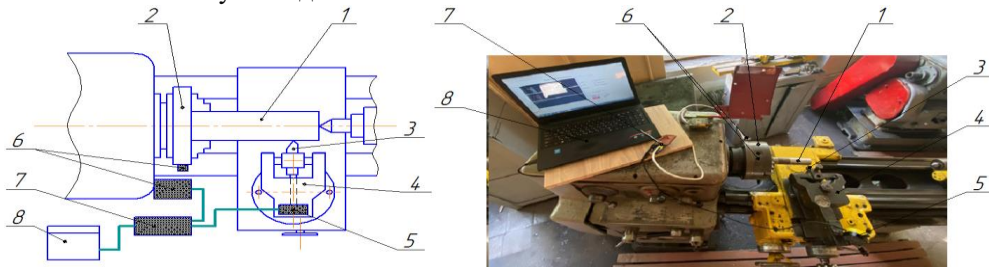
Стенд для дослідження сили різання на токарно-гвинторізному верстаті: а – схема станда; б – загальний вигляд станда; 1 – заготовка для токарного обробітку; 2 – трьохкулачковий самоцентруючий патрон; 3 – токарний різець; 4 – динамометр кручення ДК1; 5 – індикатор з цифровим відліковим пристроєм; 6 – давач обертів; 7 – плата Arduino Mega 2560; 8 – ПК.
